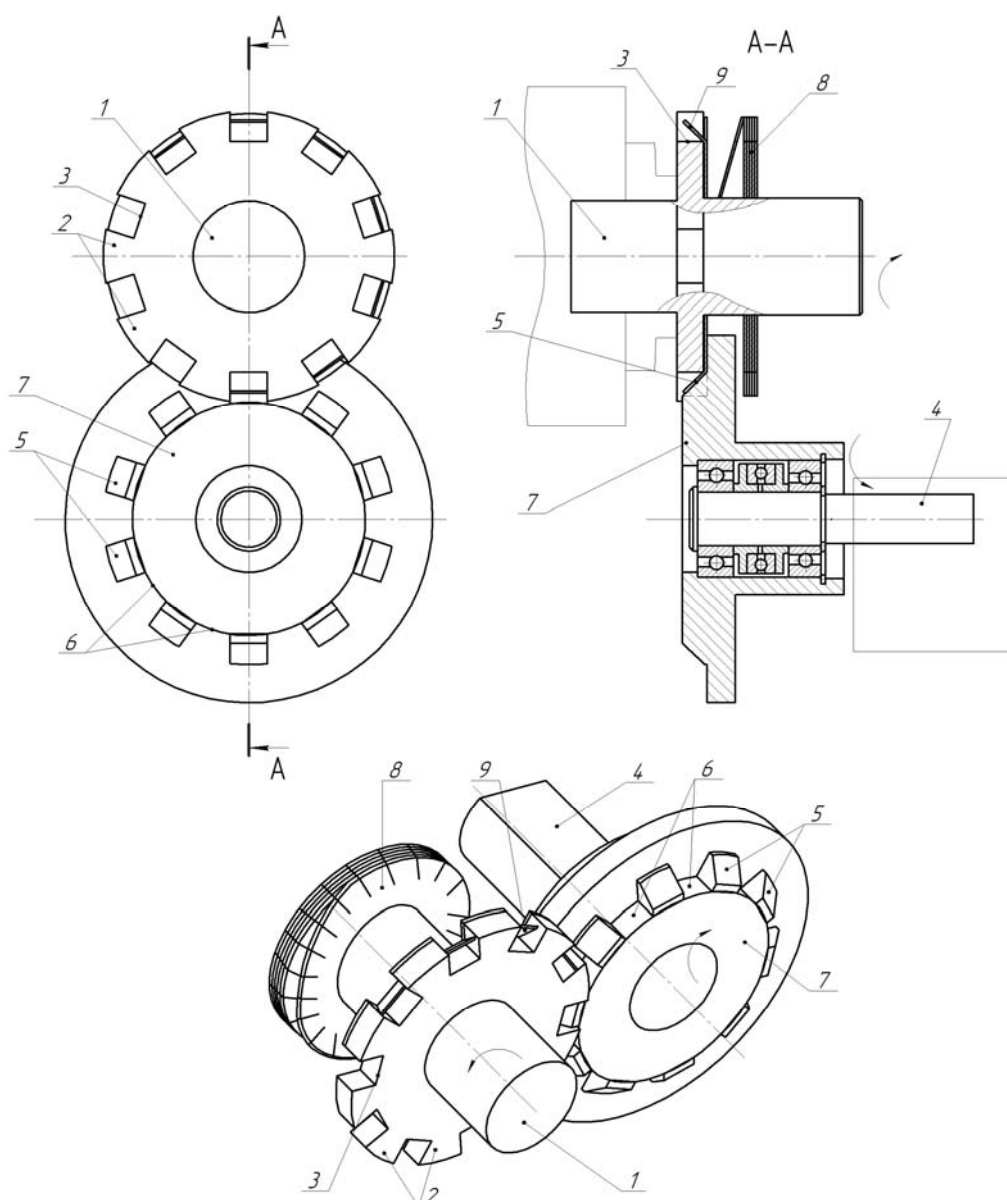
Пристрій для виготовлення ножів-подрібнювачів на гвинтовій заготовці
